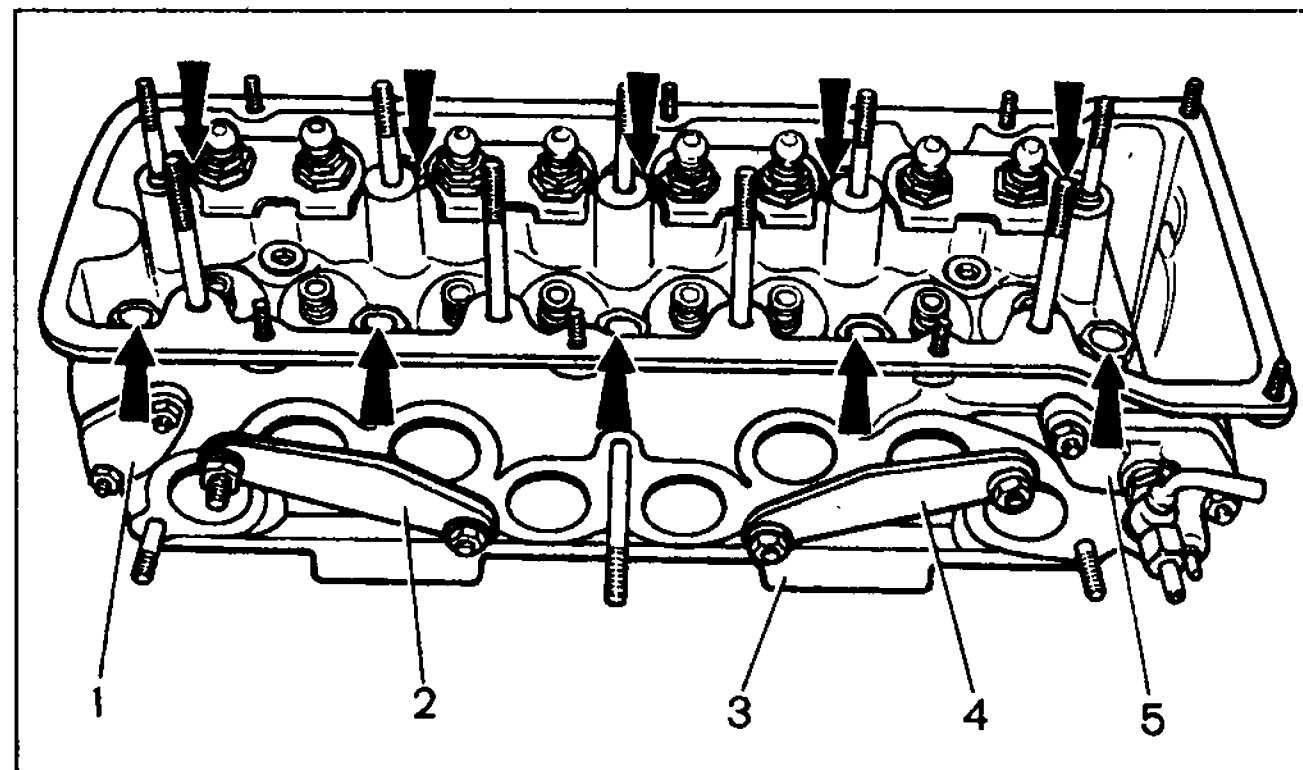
Проверка герметичности головки цилиндров на приспособлении А.60334:
